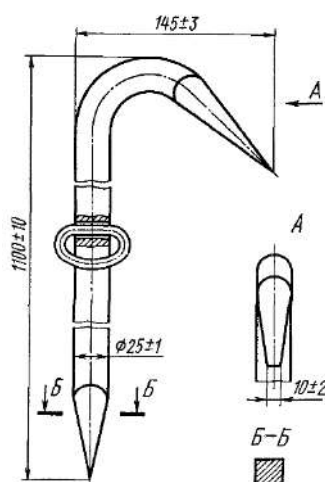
Форма и основные размеры ЛПЛ согласно ГОСТ 16714
